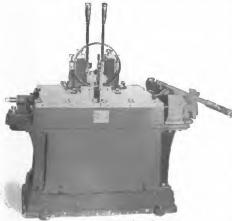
Reifenschweissmaschine Type 20 A.
